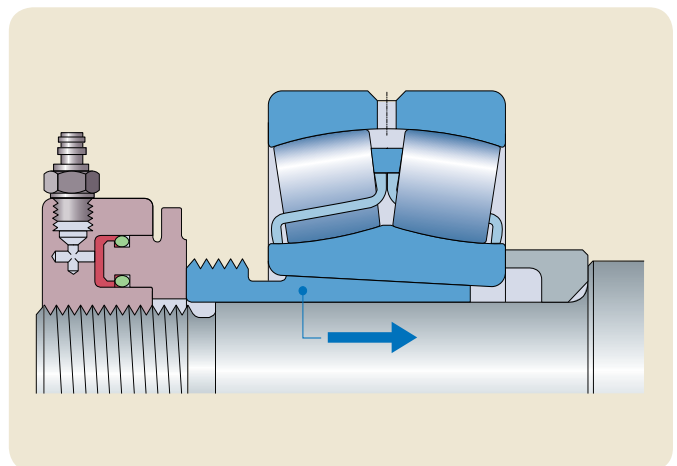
Roulement monté sur un manchon de démontage qui est poussé entre le roulement et l'arbre.
